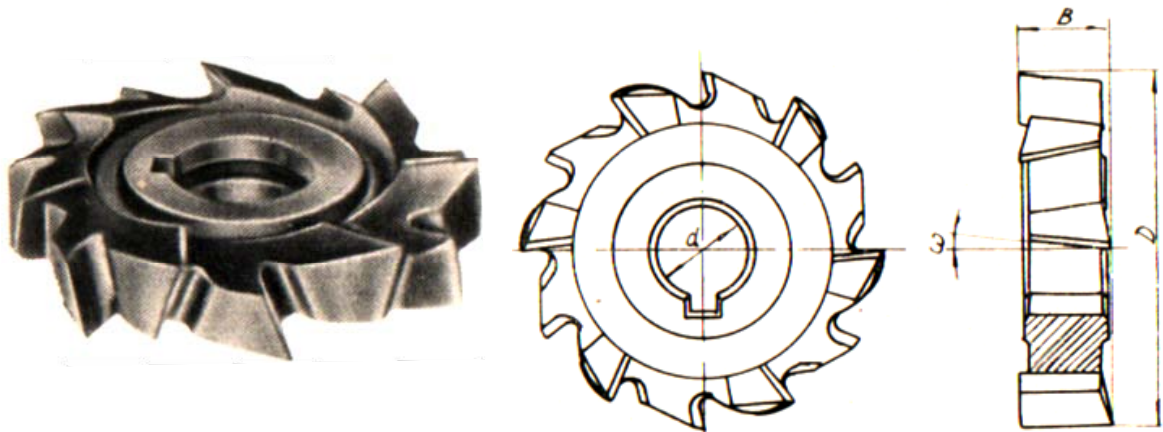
Современная конструкция цельной дисковой фрезы с трехсторонней схемой резания
